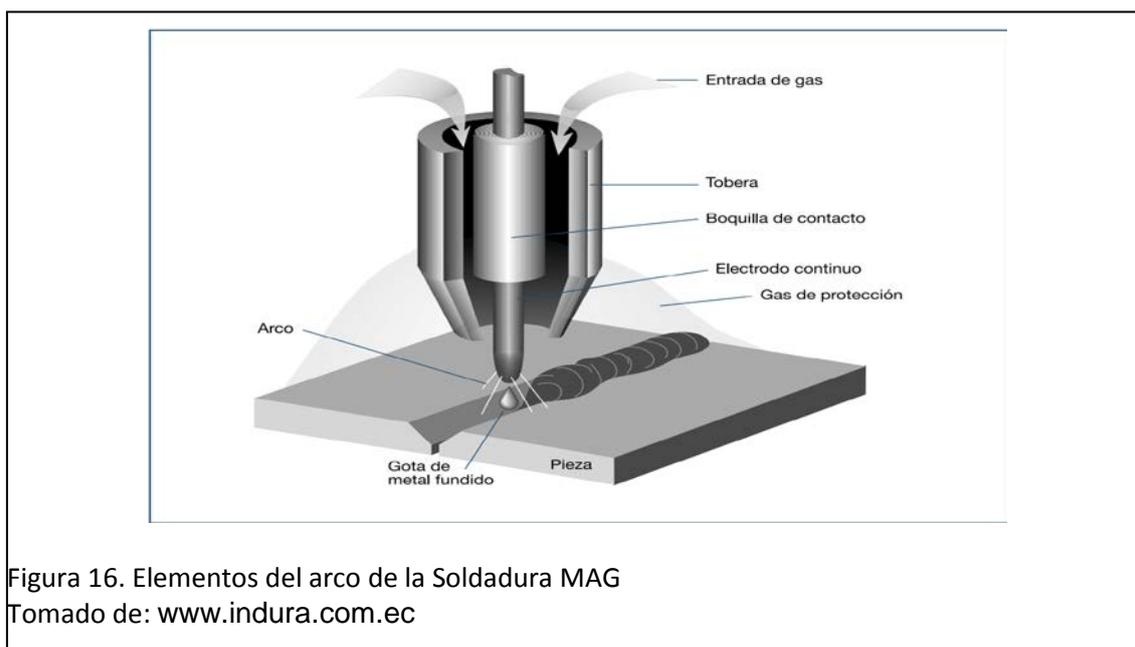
Elementos del arco de la Soldadura MAG
